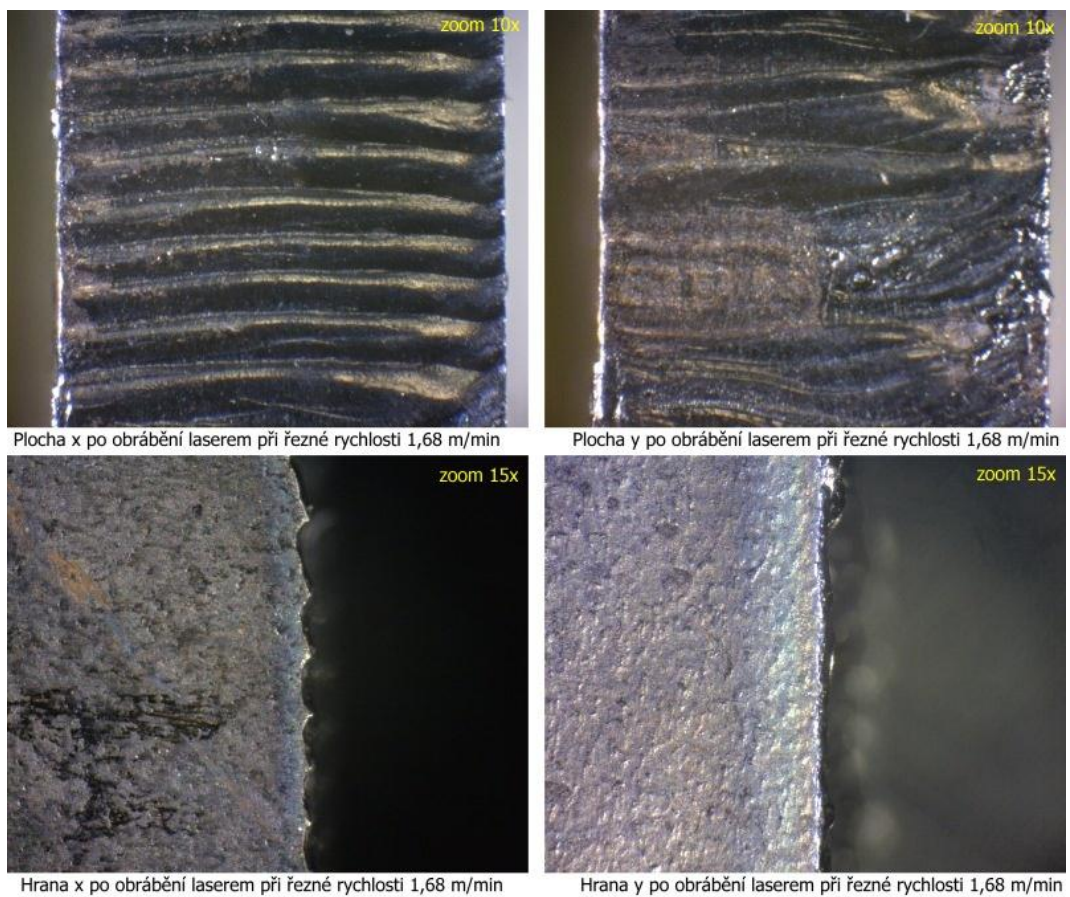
Snímky z mikroskopu vzorku 4 obráběného laserem - materiál 11 375
